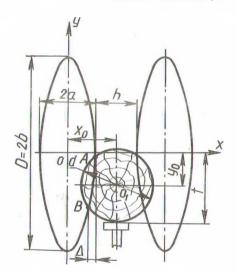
Схема образования поперечного сечения пиломатериала при установке фрез с разворотом.
